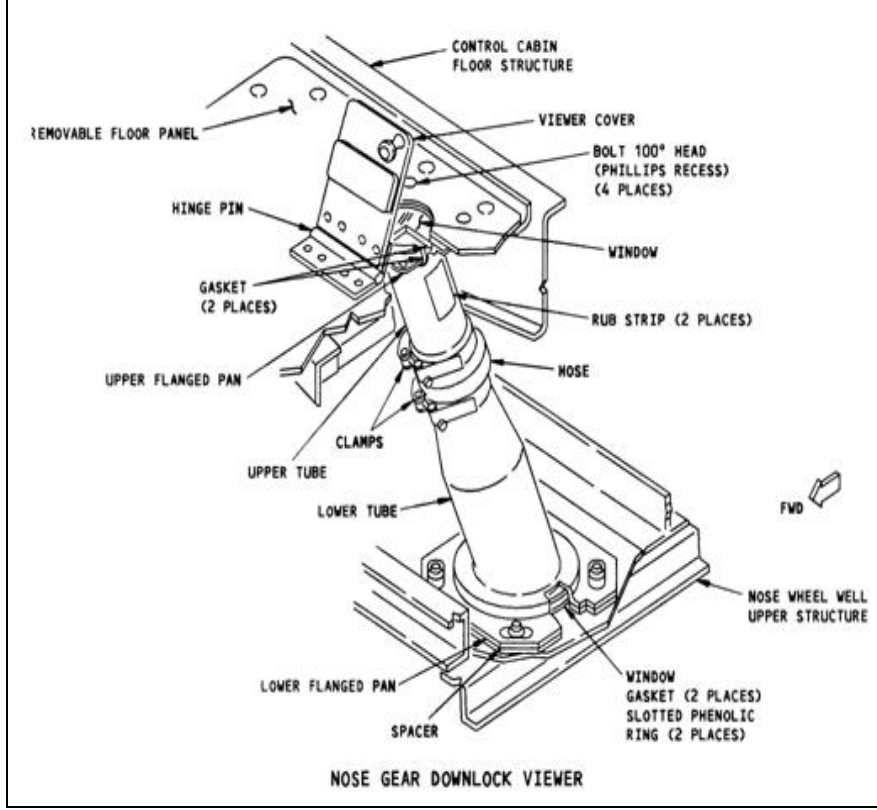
Ana iniş takımı gözlem camı ve parçaları
